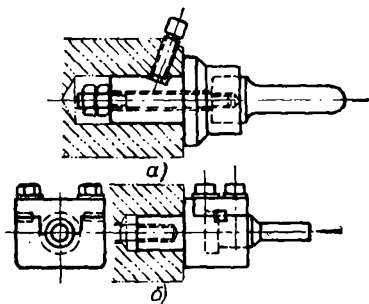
Способы крепления пуансонов в пуансонодержателе: а — крепление упорными болтами; б — крепление стяжными болтами
